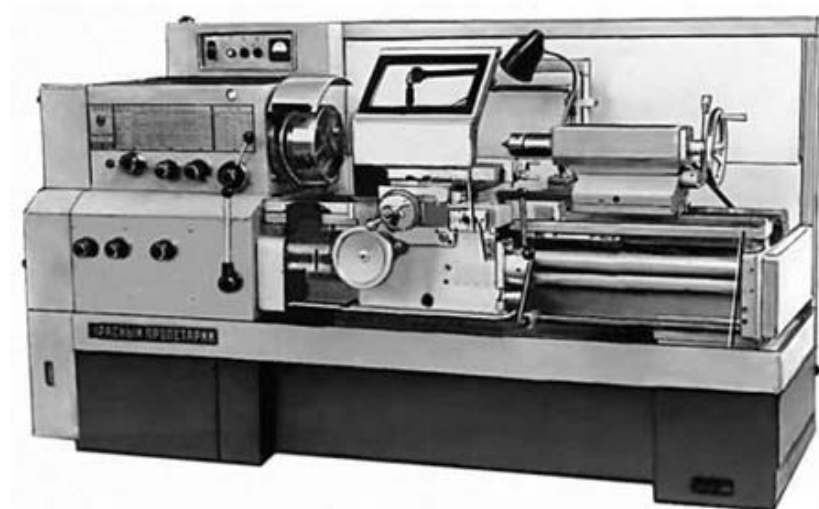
Токарно-гвинторізний верстат мод. 16K20
